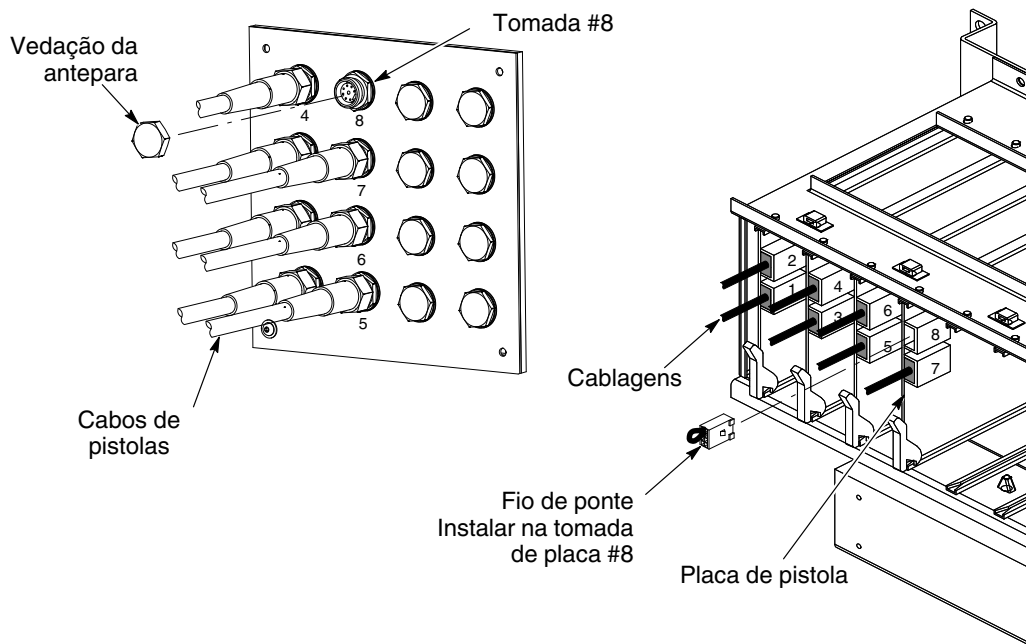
Instalação de vedações e fios de ponte - Exemplo mostrando um sistema de 8 pistolas utilizando 7 pistolas
